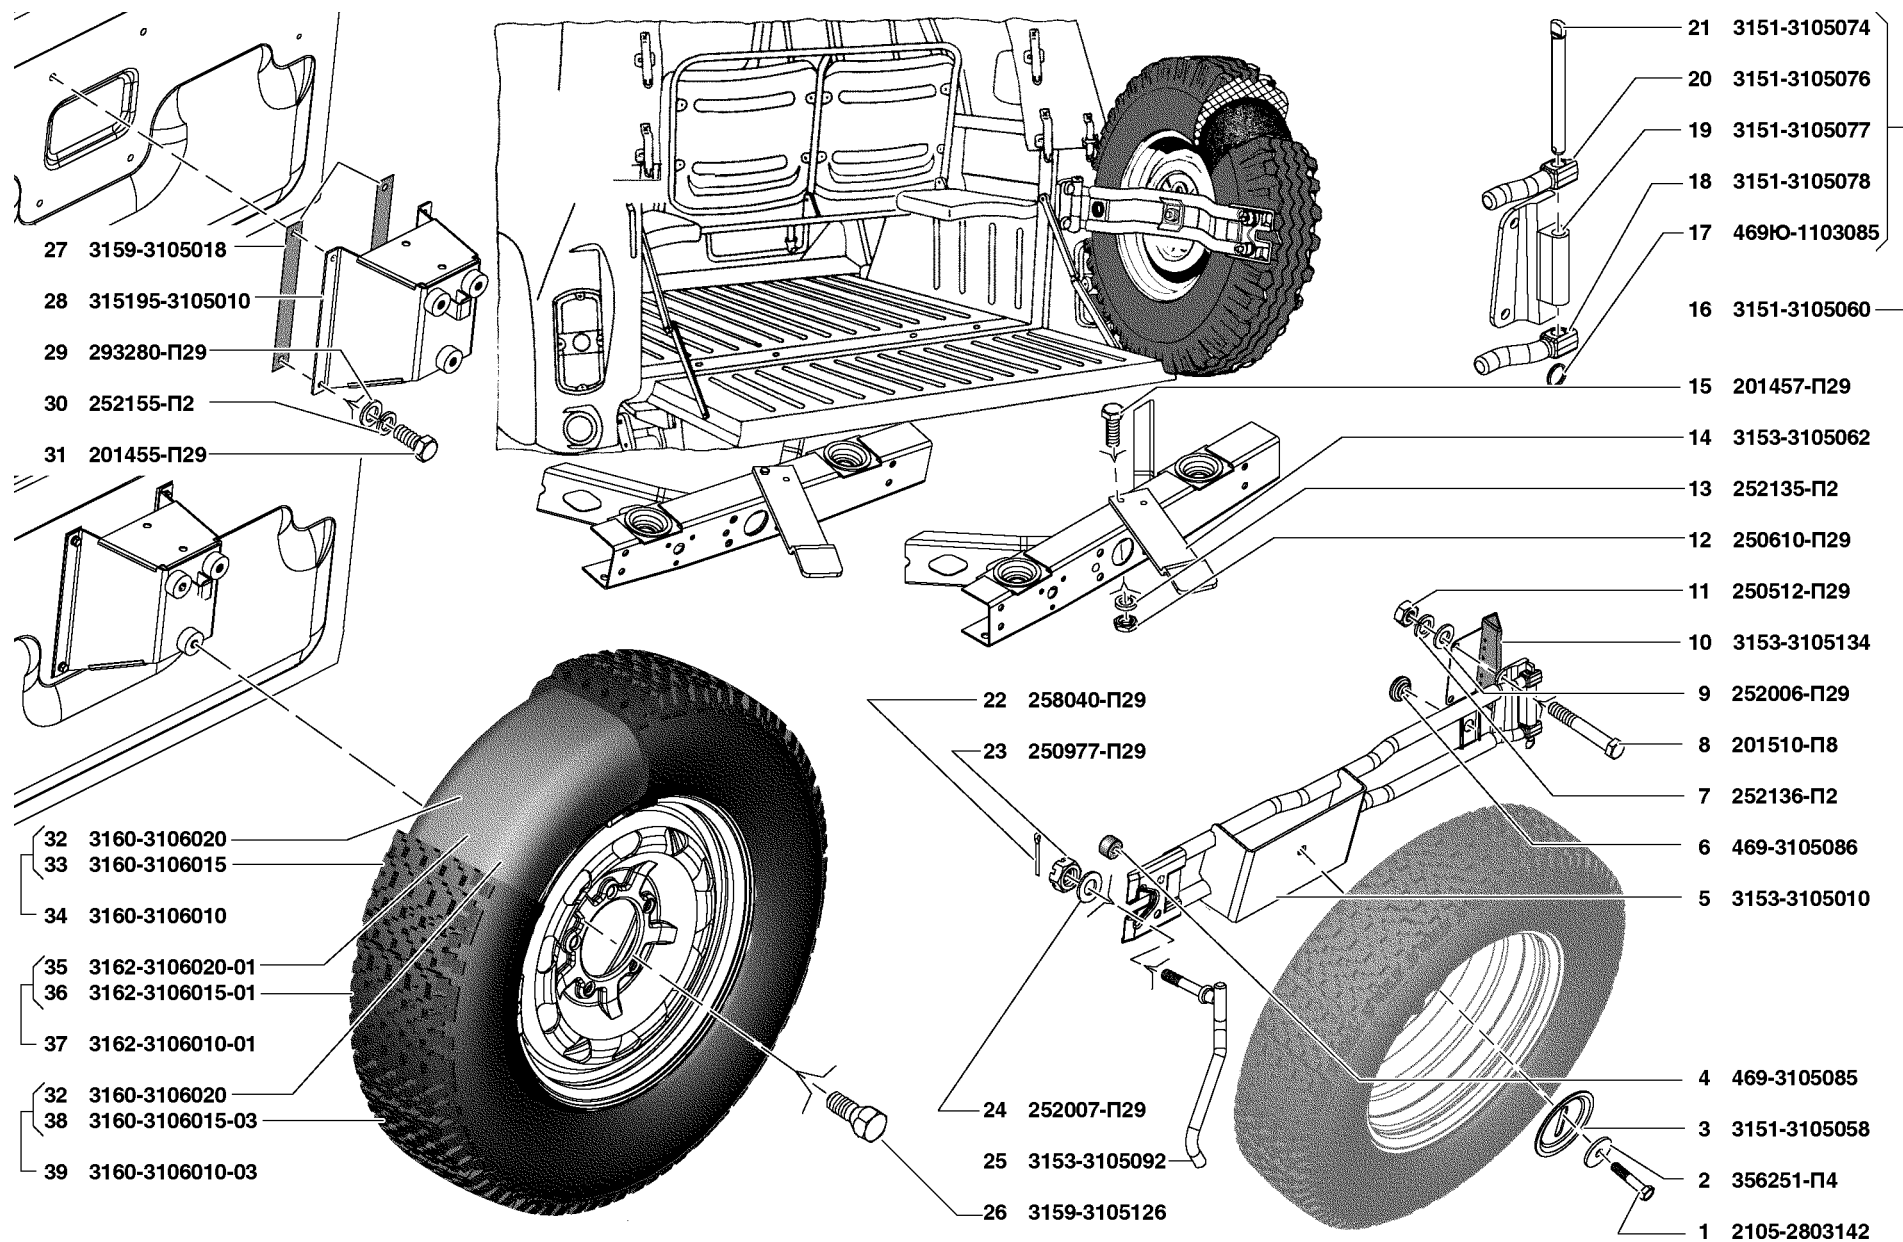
Держатель запасного колеса (3105), покрышки и камеры (3106)
